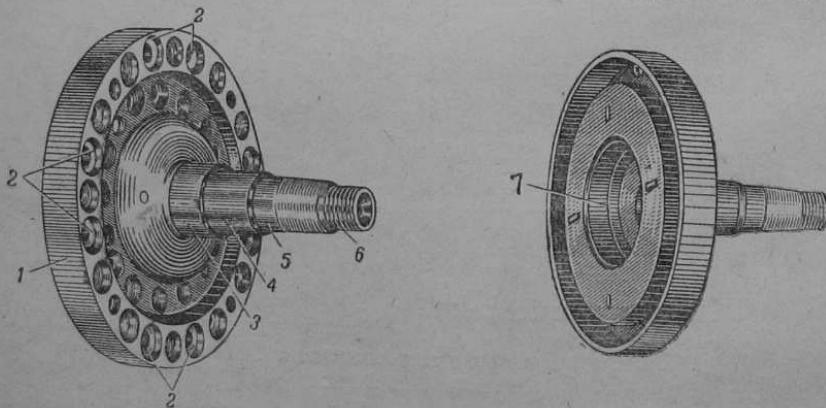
Ось ротора нагнетателя двигателя С2Б:
